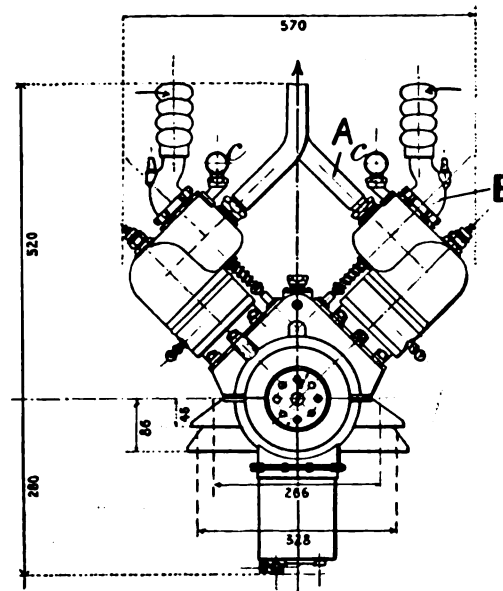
Zeichnung des Motors »Antoinette«. Stirnansicht. E Einlaßventile mit Lufteinlaß. A Auspuffrohe. C Wasserauslaß.
